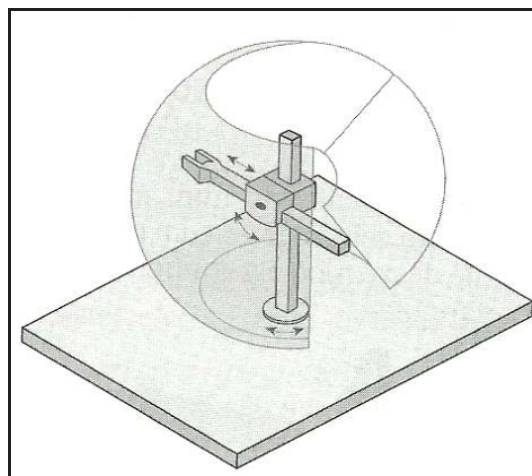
Vista frontal e superior de um robô de coordenadas cilíndricas
